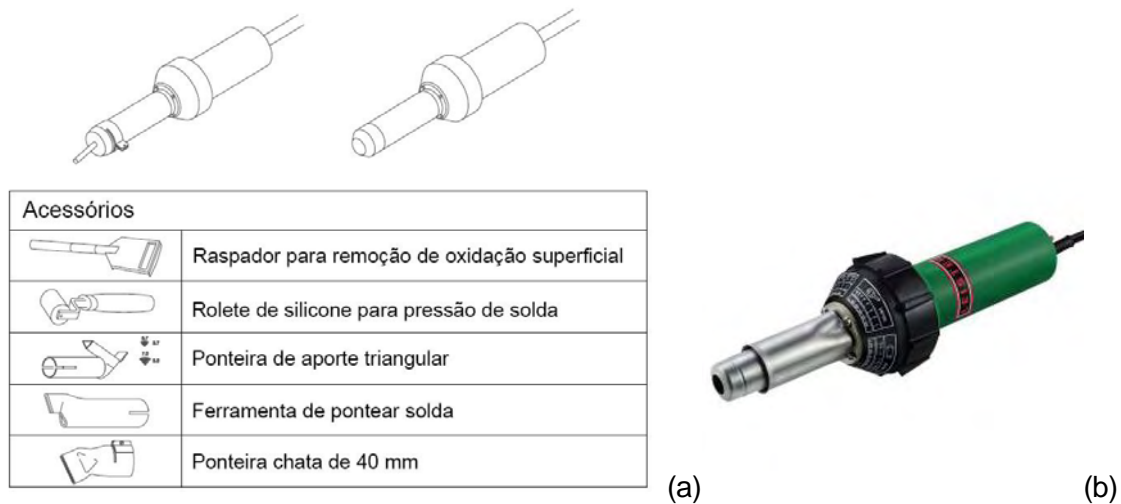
Acessórios de uma máquina de soldar de ar quente (a) e imagem real da mesma (b).
